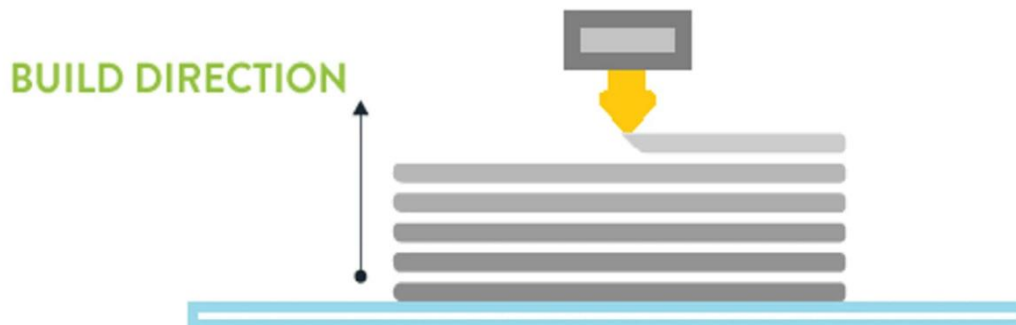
Hauteur de couche pour les pièces imprimées en 3D
